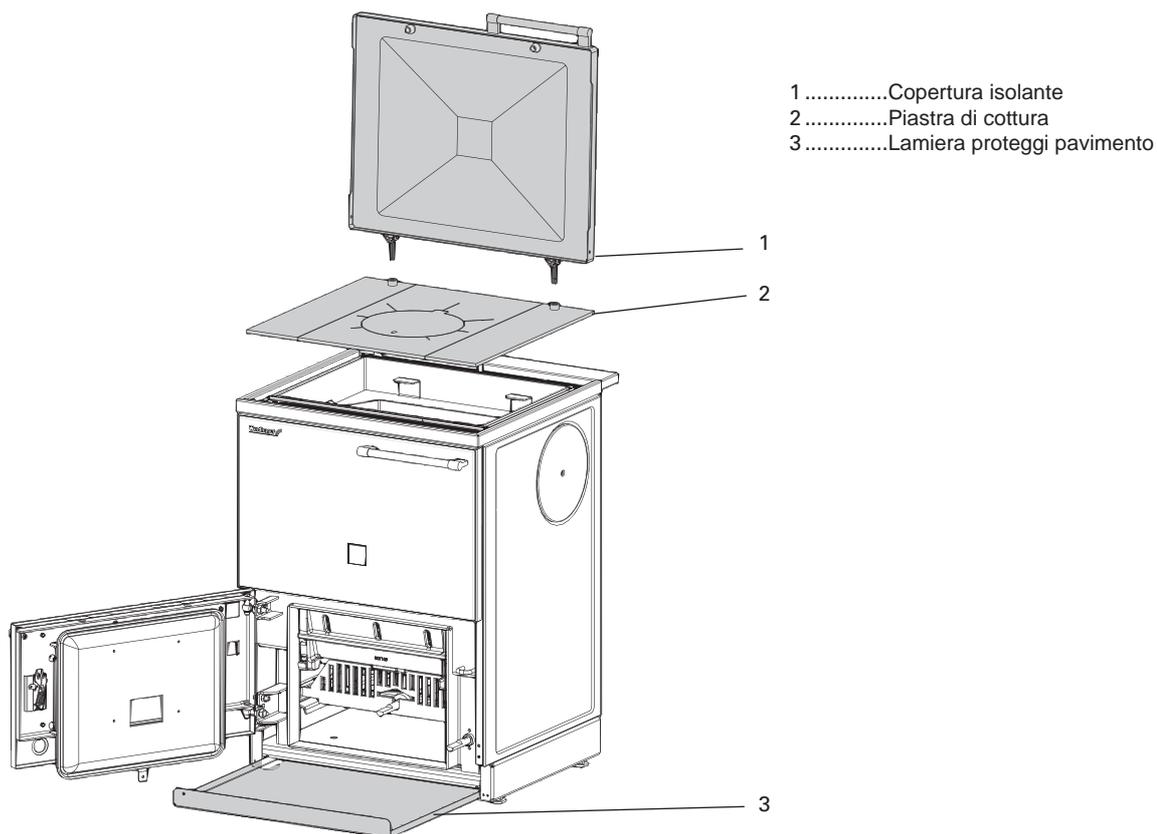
Montaggio della piastra di cottura, della copertura isolante e della lamiera proteggi pavimento.
